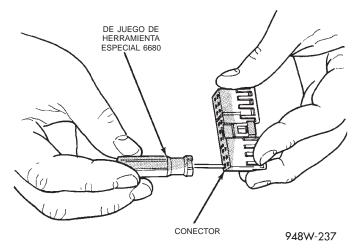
Desmontaje del terminal utilizando la herramienta especial
